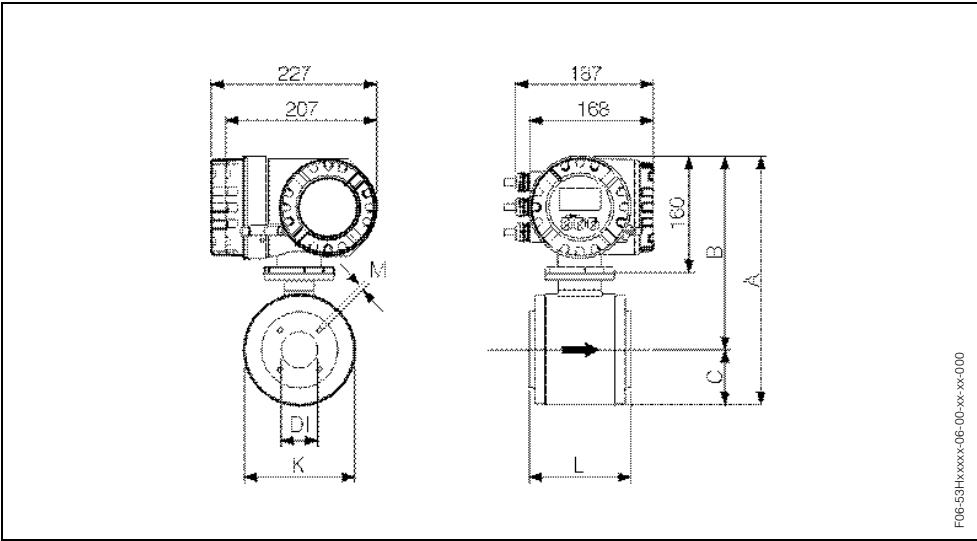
Dimensiones del Promag H / DN 40...100 (versión compacta, cabezal de aluminio para montaje en campo)
